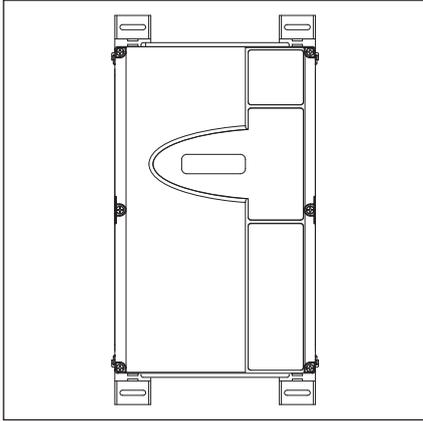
Steuerungsgehäuse mit vertikal befestigten Montagefüßen
